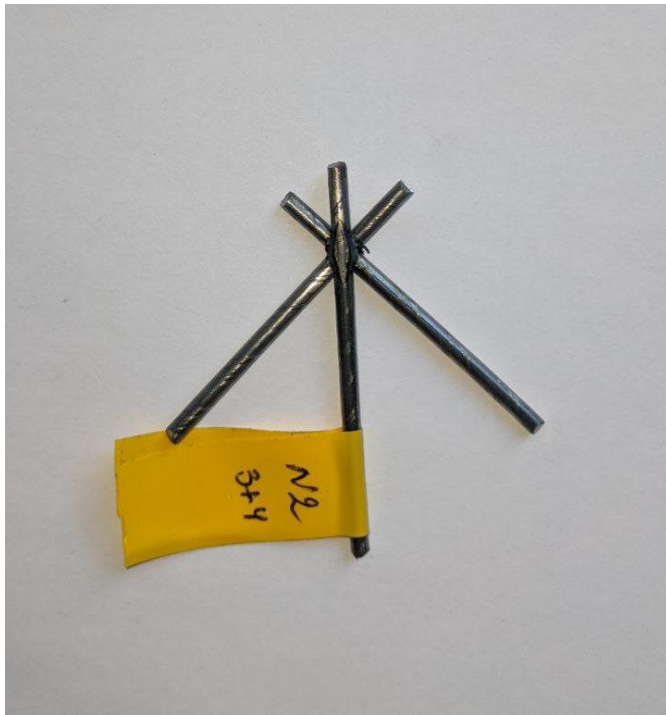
Зварювання трьох дротів з часом зварювання 3+4
